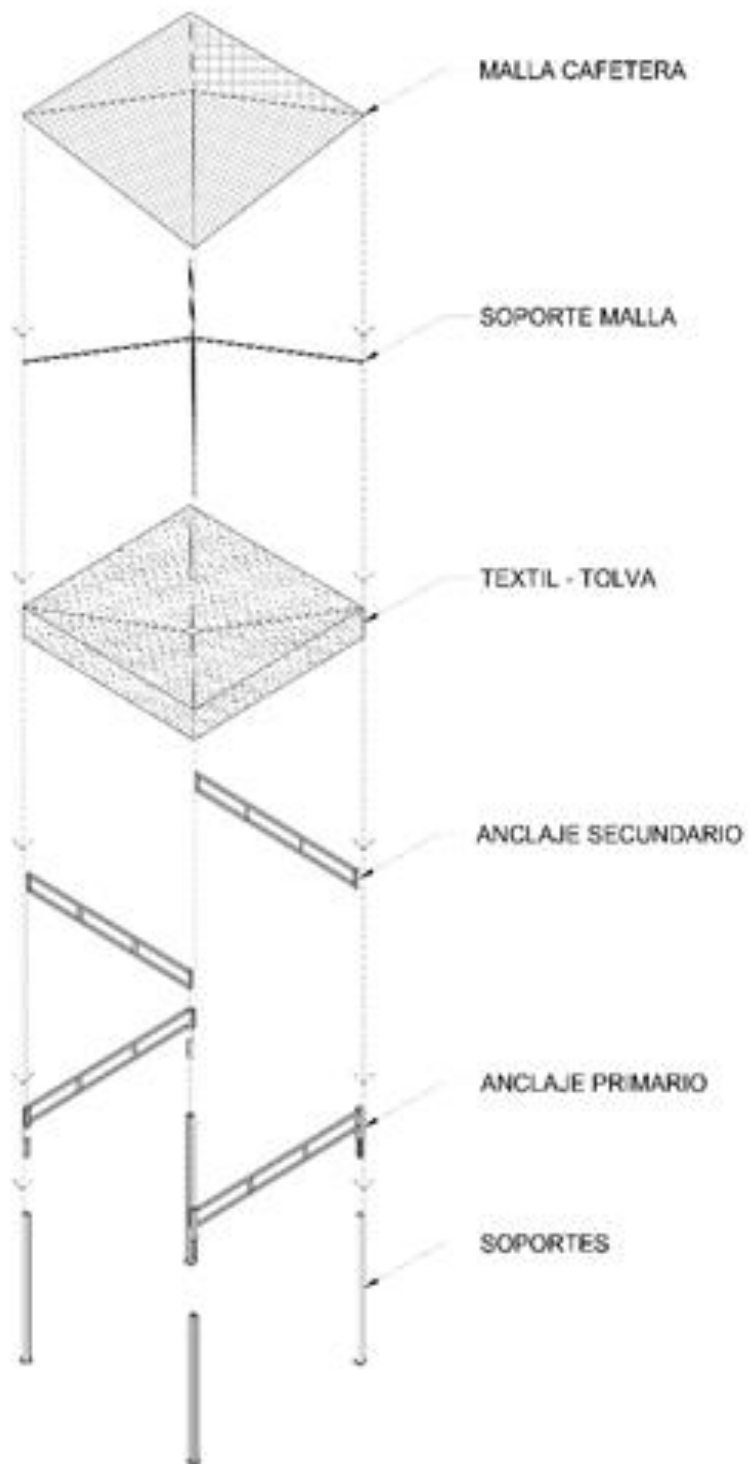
Proceso de Armado de la Estructura Metalica de la Tolva.
